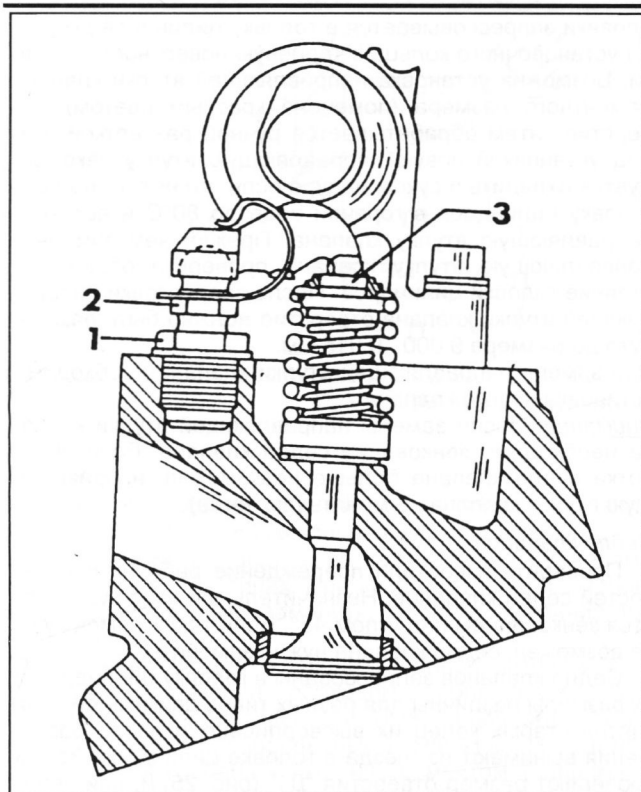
Разрез головки цилиндров. Зазор клапанно-го механизма измеряется между кулачком распределительного вала и коромыслом.. 1 - опора резьбовая, 2 - болт регулировочный, 3 - толкатель.
